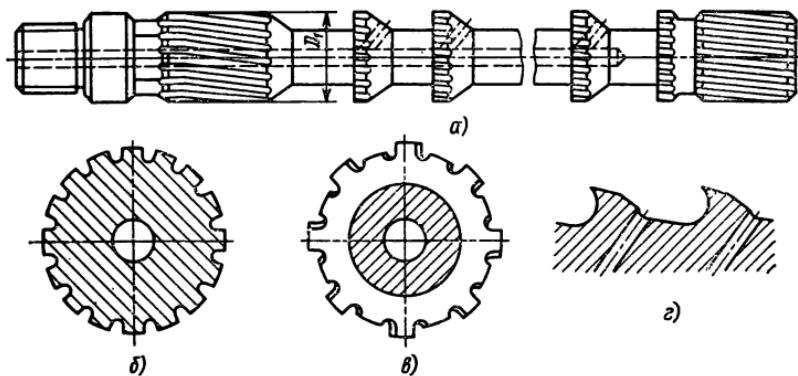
Протяжка шлицевинтовая с кольцевым зубом и шахматно-шлицевой схемой резания:
